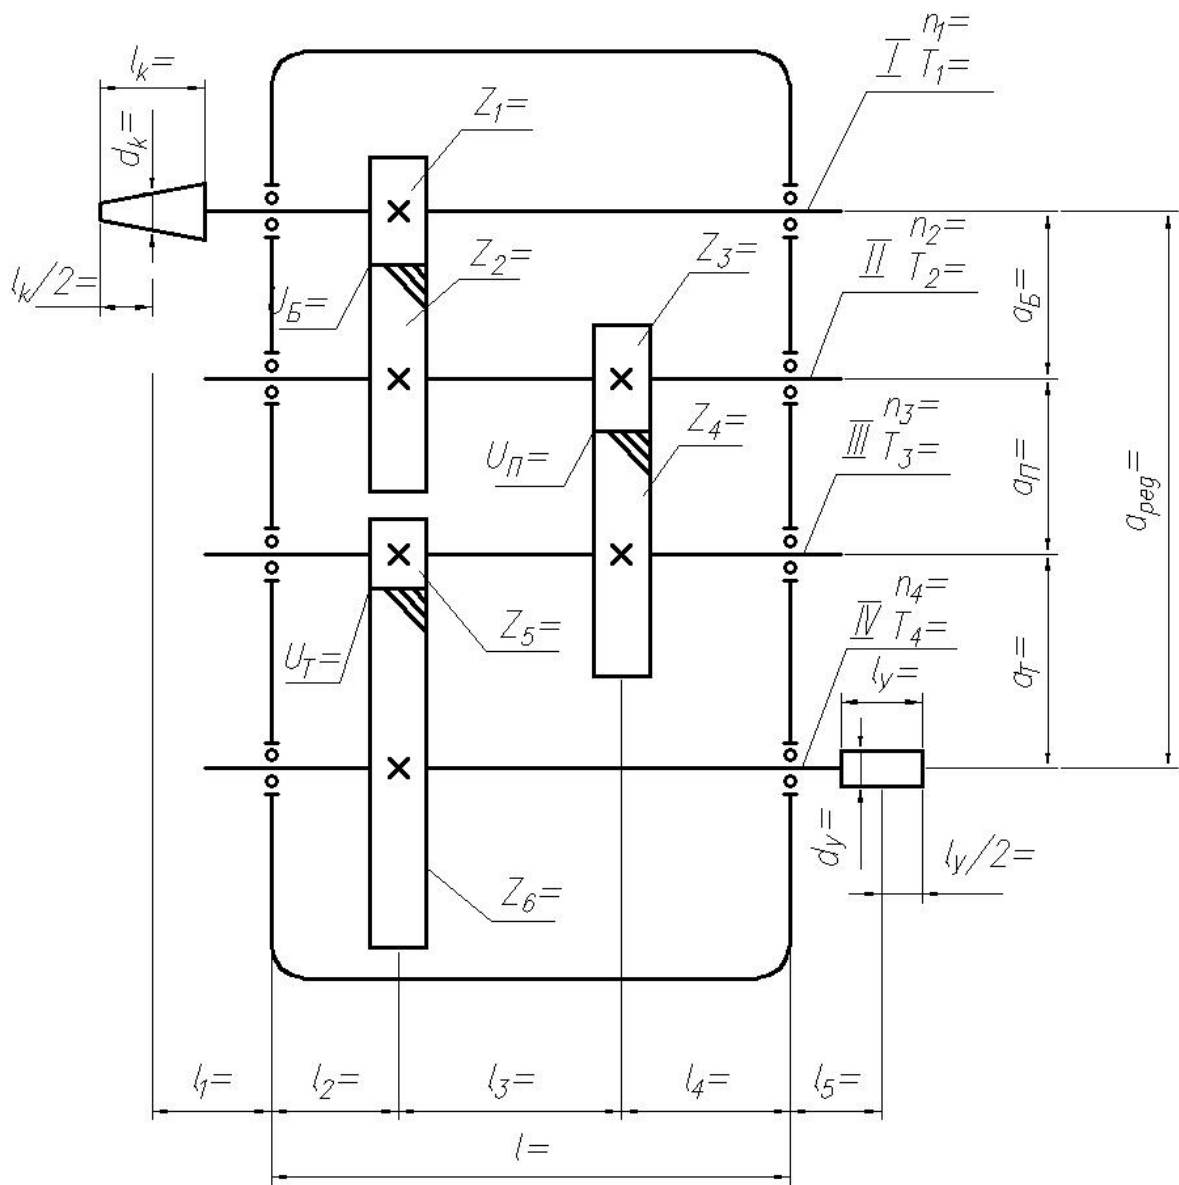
Кинематическая схема трехступенчатого зубчатого редуктора:
